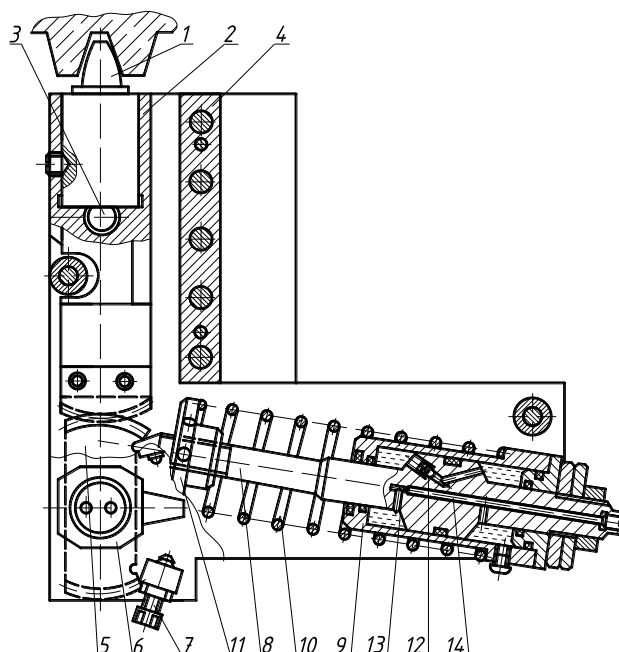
Устройство для обкатывания роликами клиноременных шкивов
